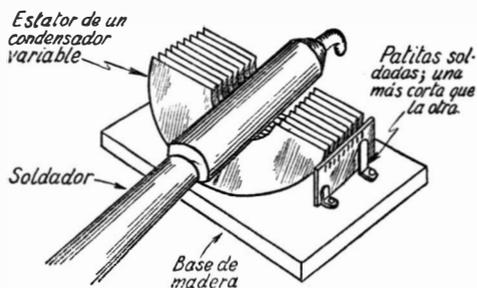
Aspecto que adquiere el posasoldador una vez terminado.
